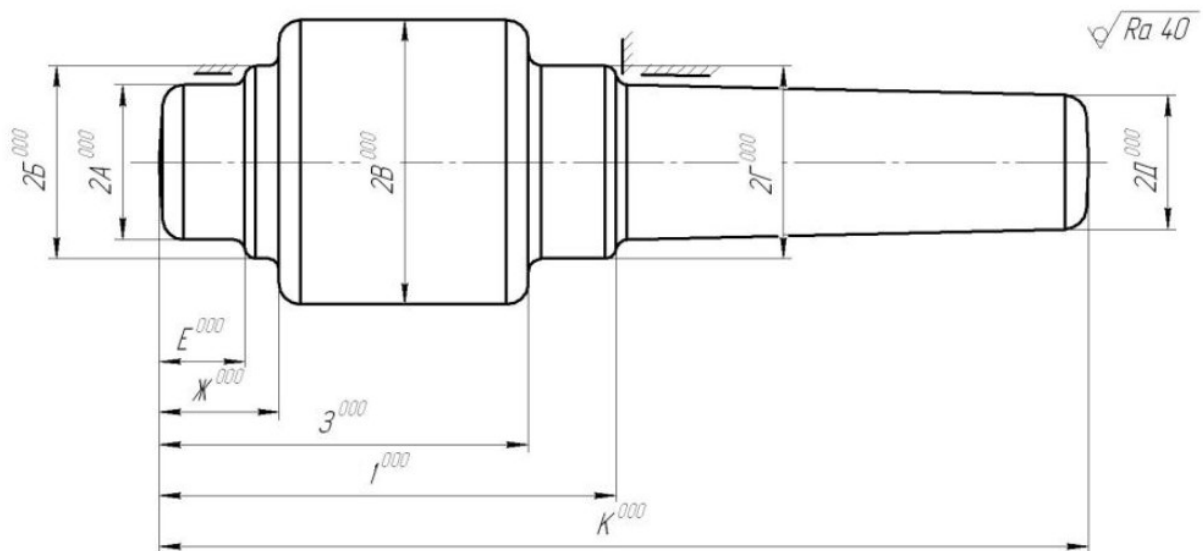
Заготовка деталі вал-шестерня редуктора SZ 121
